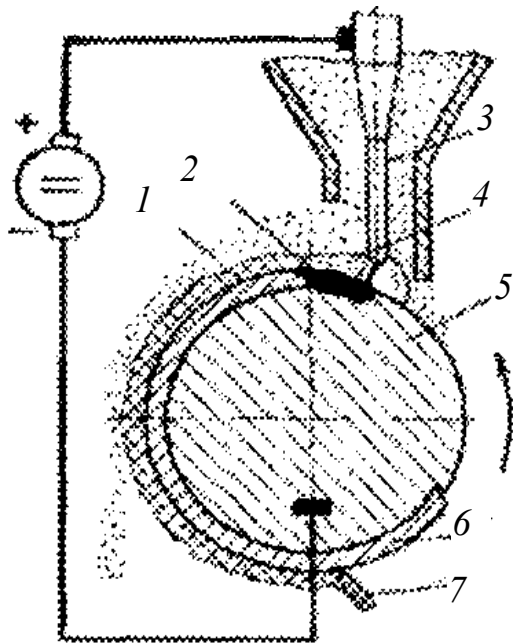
Схема наплавлення: 1 — флюс; 2 — рідкий метал; 3 — електрод; 4 — струмопідвід; 5 — газовий міхур; 6 — валик; 7 — шлакова корка
